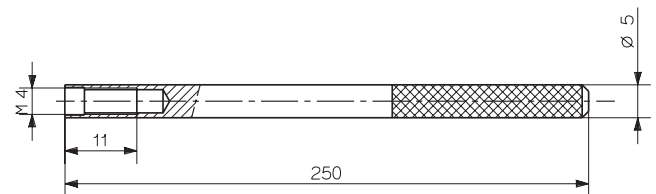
Ausziehwerkzeug für Blindsensor Typ 1319
